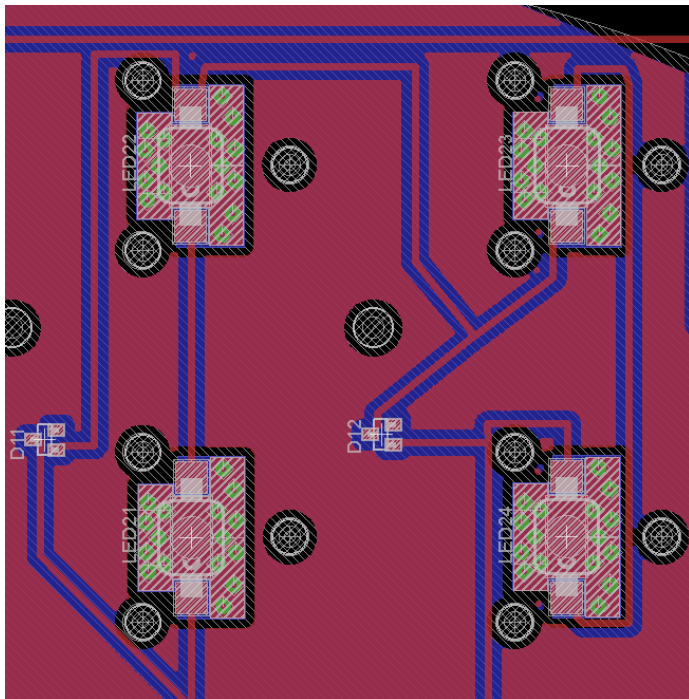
Board Layout mit LED Thermal Vias Pad Design
